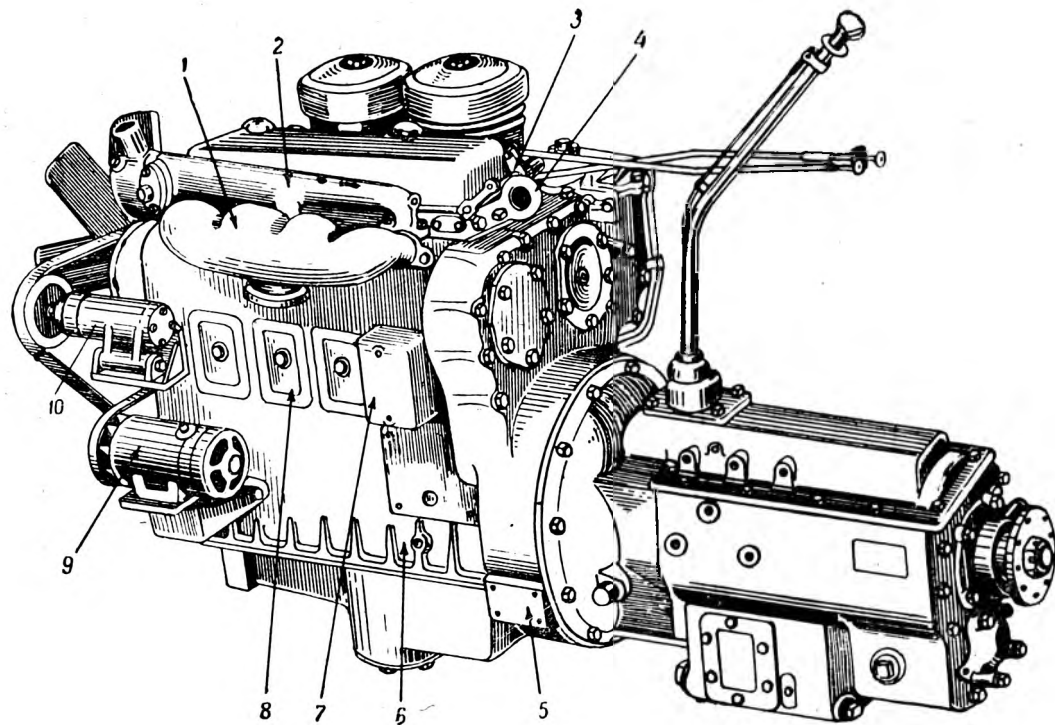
Двигатель Джи-эмси (вид с левой стороны):
